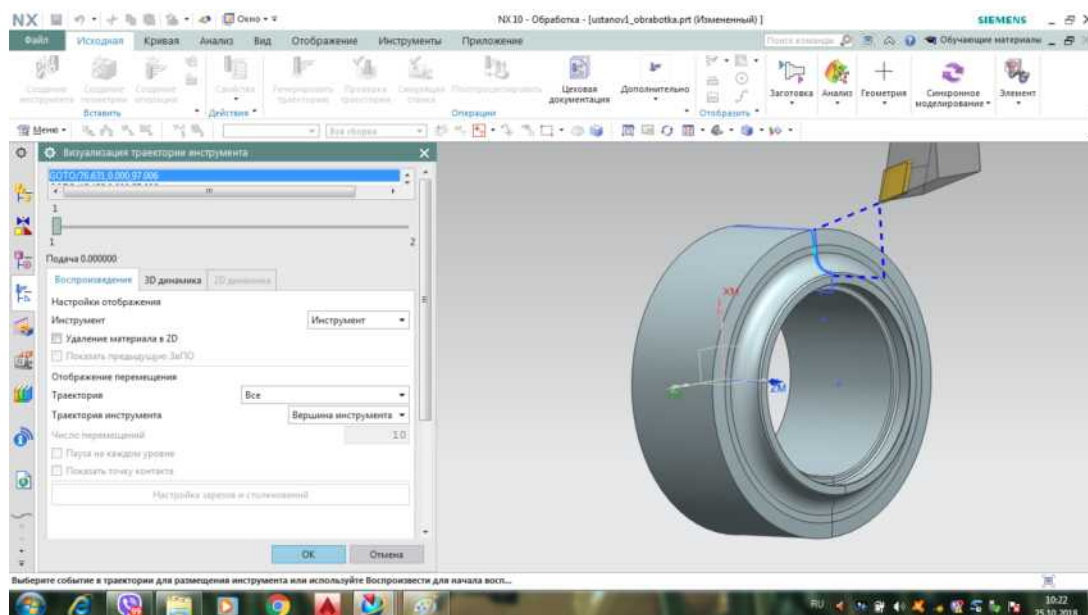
Траекторія обробки з інструментом установка 1, перехід 2
